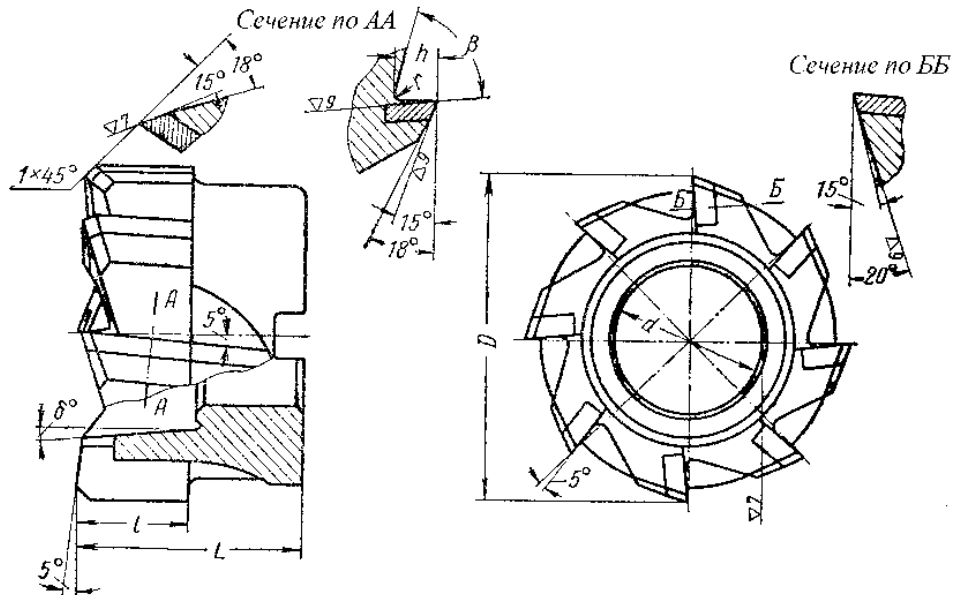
Торцовая фреза с напаянными пластинами твердого сплава
